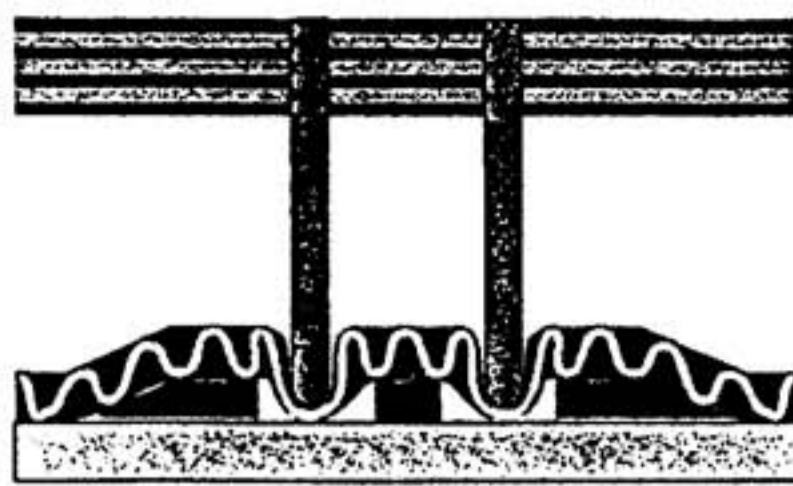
Биговка на матрице с двумя параллельными биговальными каналами
